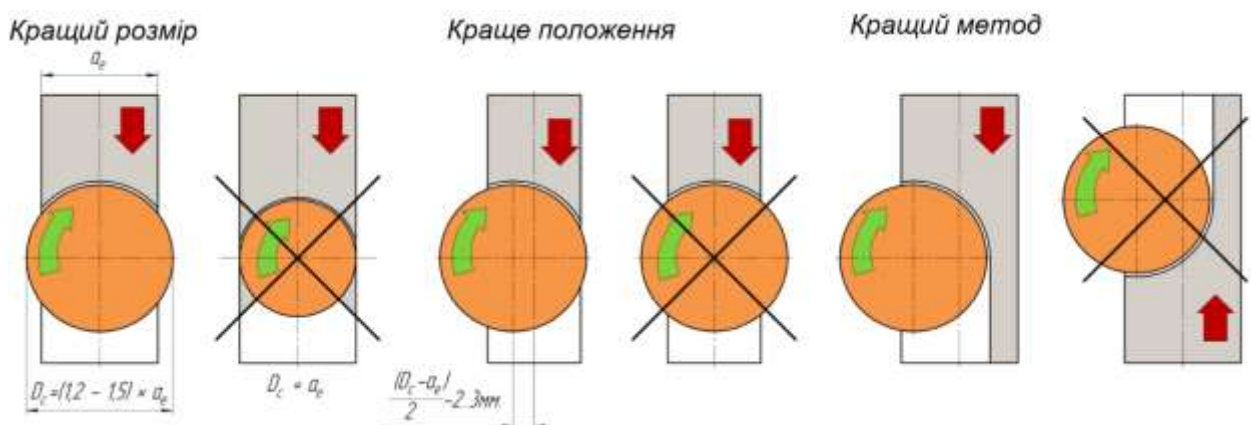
Варіанти розташування фрези щодо заготовки
